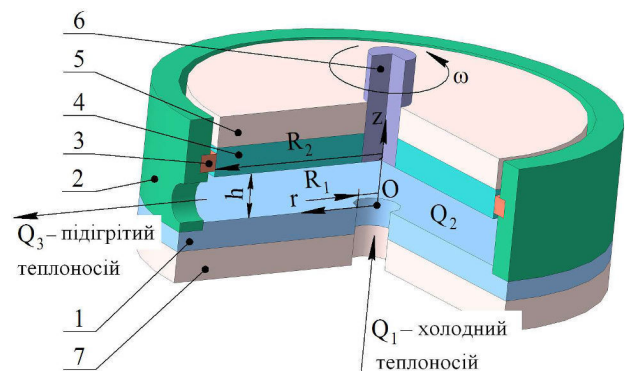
Розрахункова схема роторно-імпульсного апарата для побудови математичної моделі: 1 – нерухомий диск; 2 – корпус; 3 – ущільнювальний елемент; 4 – обертовий диск; 5, 7 – теплоізоляційні пластини; 6 – вал
